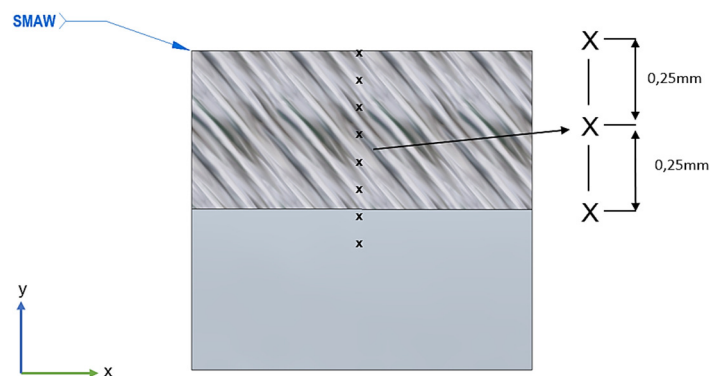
Ilustração da aplicação de revestimento duro em um corpo de prova soldado.
